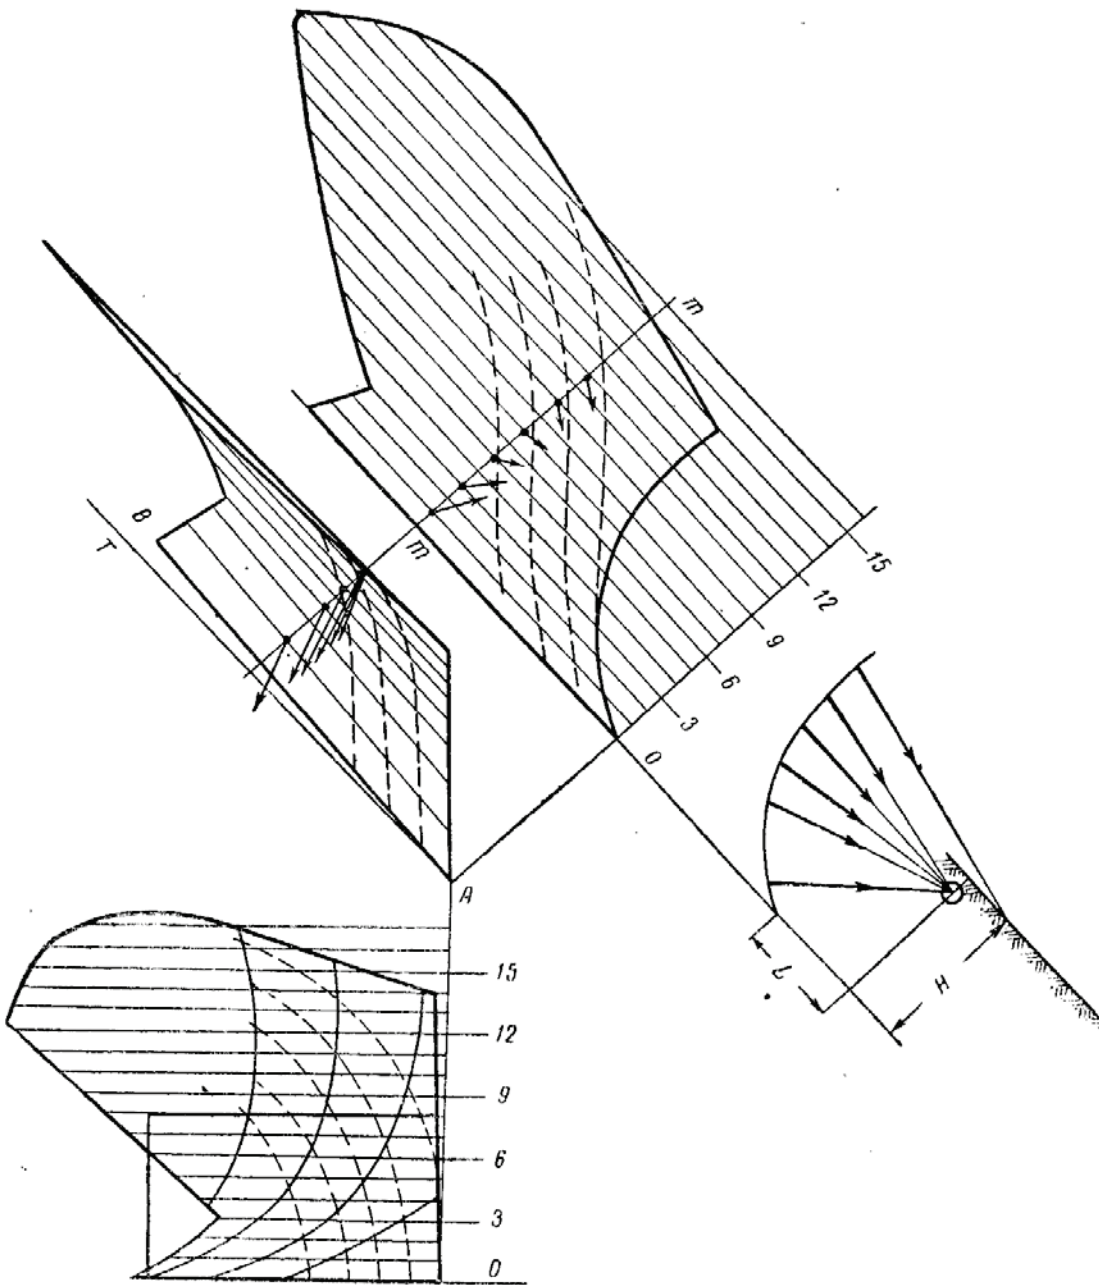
Графічний аналіз поверхні плужного корпусу 5К35
